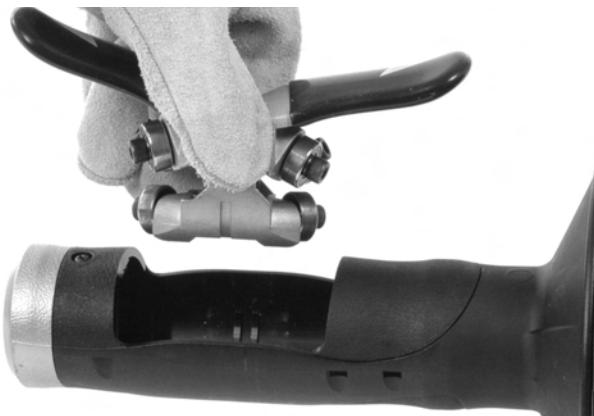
В – Снятие механизма автоподачи AUTOFEED с корпуса
